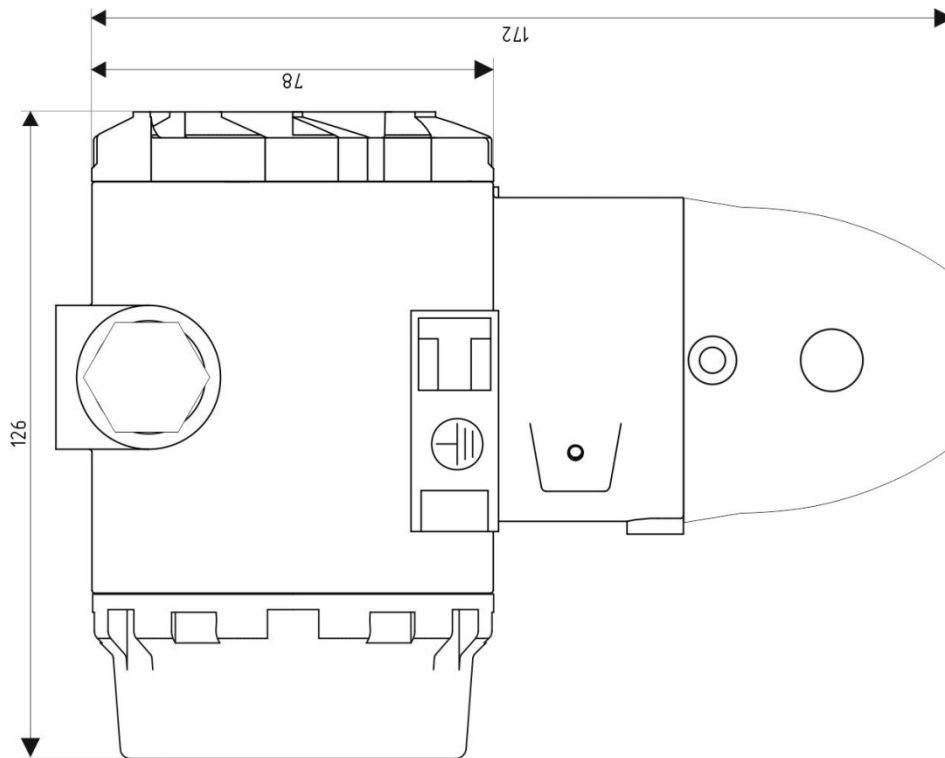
Габаритный чертеж ИКГС-ВР42-Г
